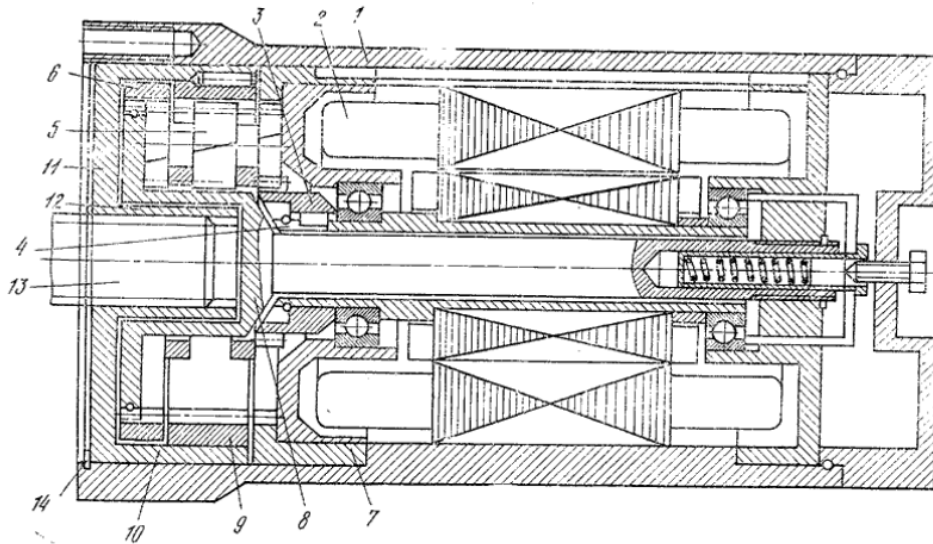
Електромеханічний ЗМ з планетарним редуктором
